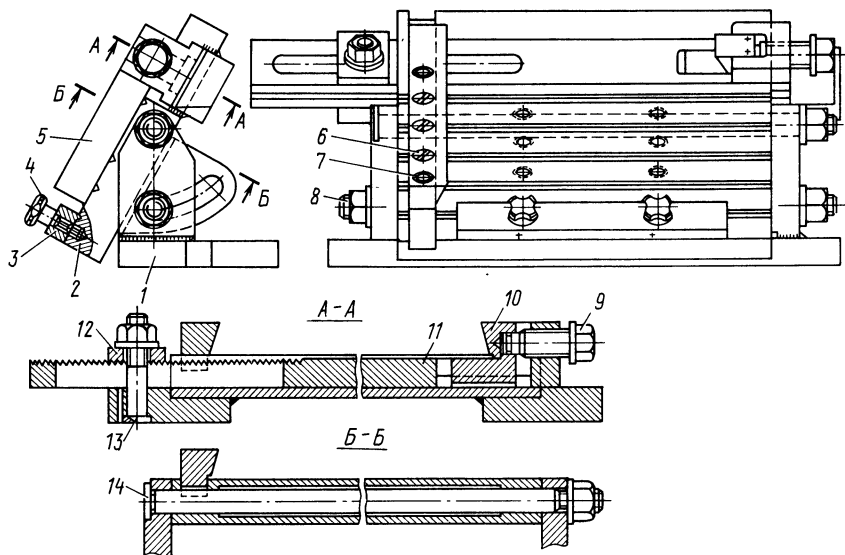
Универсальное приспособление для фрезерования фасок и скосов
